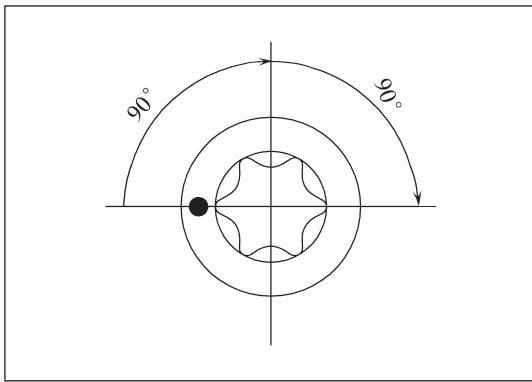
Затяжка болтов головки блока цилиндров
